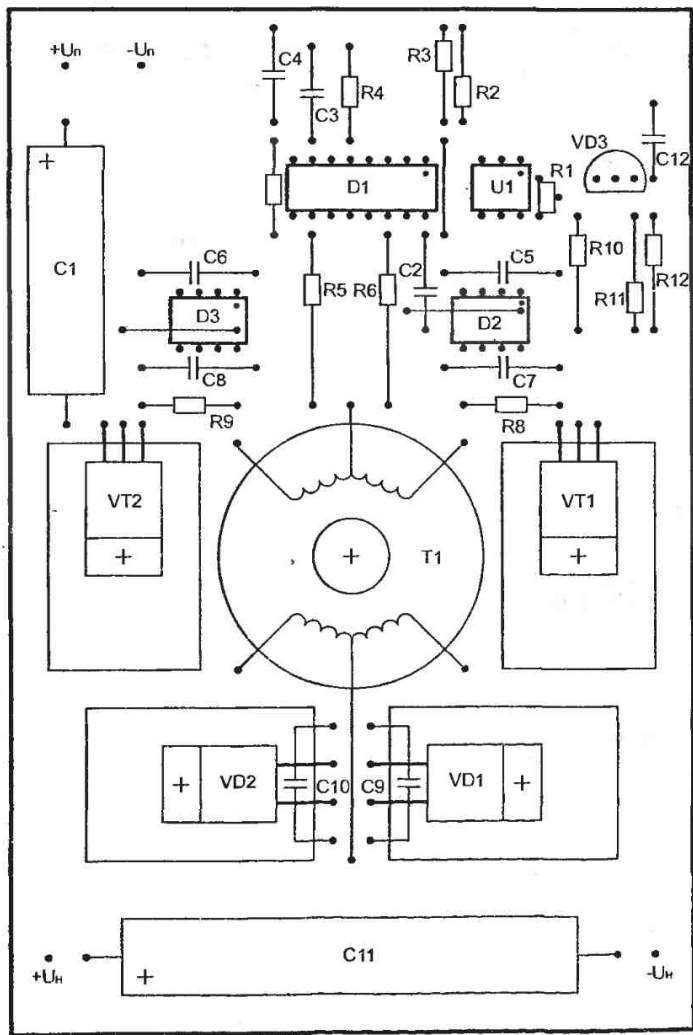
Сборочный чертеж печатной платы преобразователя
